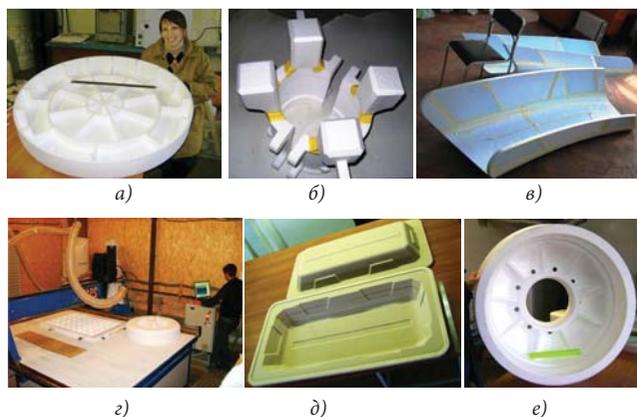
Примеры моделей, полученных на 3-D фрезере: а) крышка контейнера для захоронения радиоактивных отходов, б) элемент конвейера, в) жёлоб с габаритными размерами больше 2 м, г) 3-D фрезер в работе, д) лоток, е) колесо.
